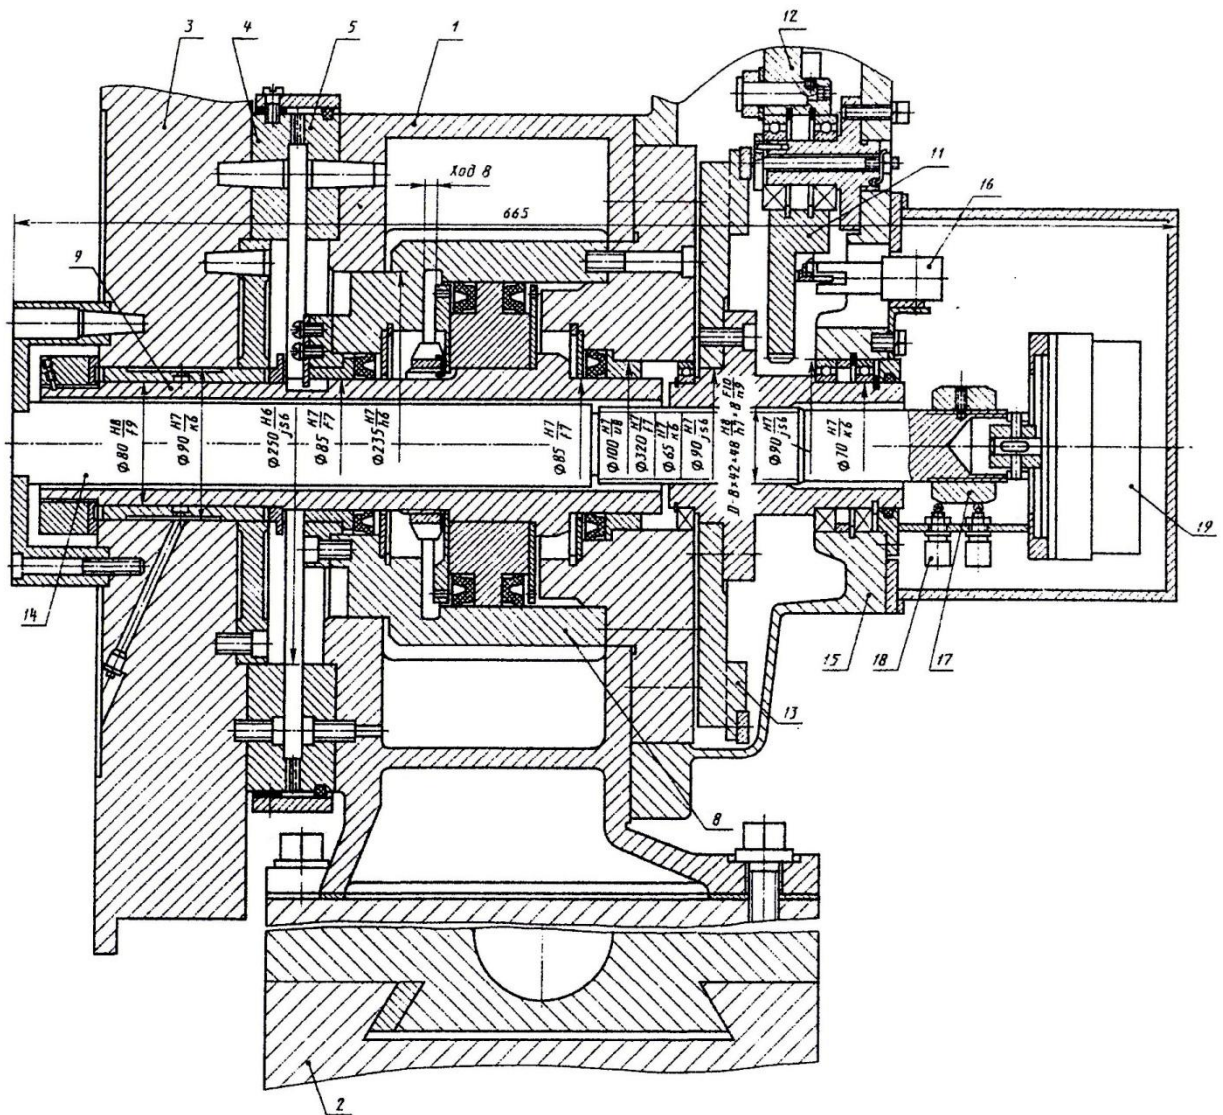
Конструкція 12ти-позиційної револьверної головки
